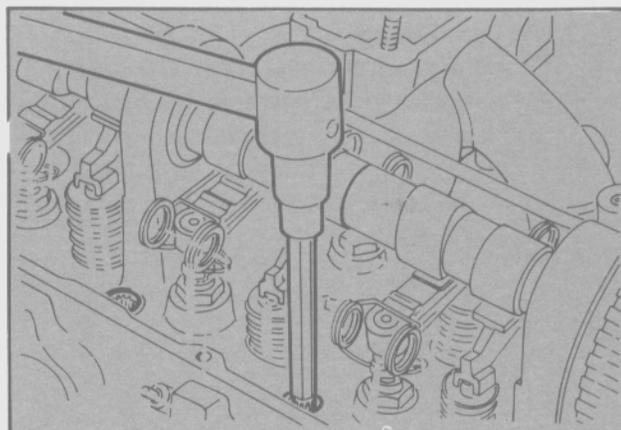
Desmontaje de los tornillos de tapa de cilindros
